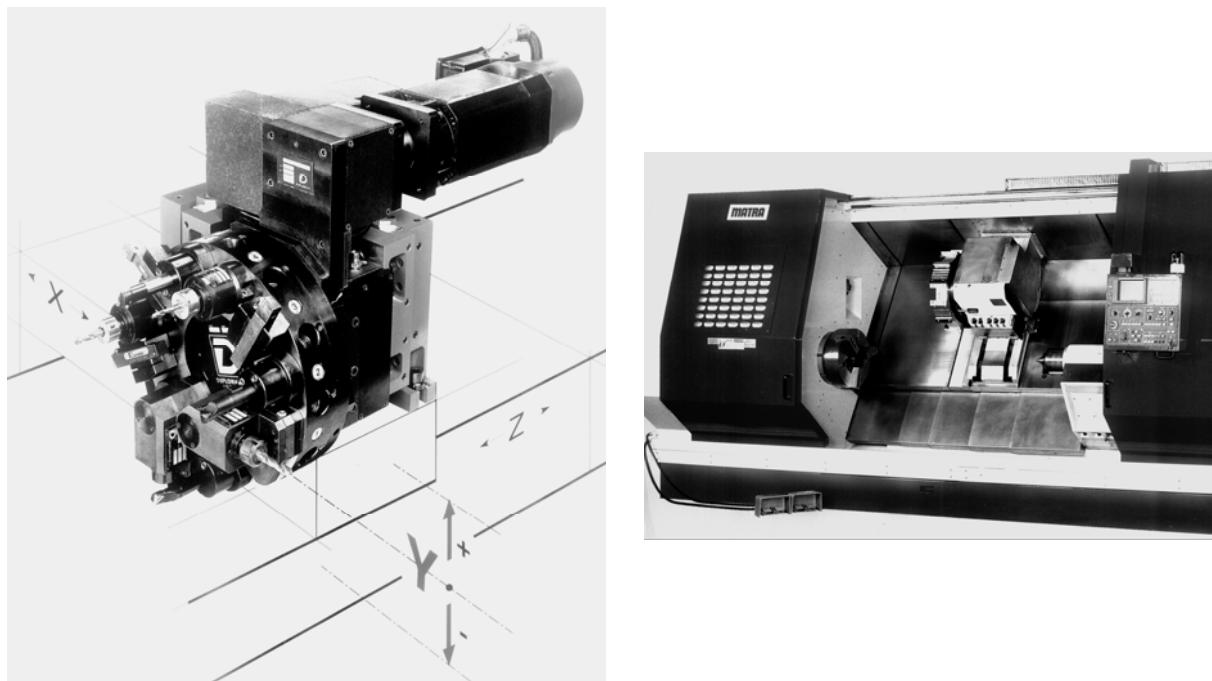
Загальний вигляд револьверної головки токарного верстата з ЧПК
